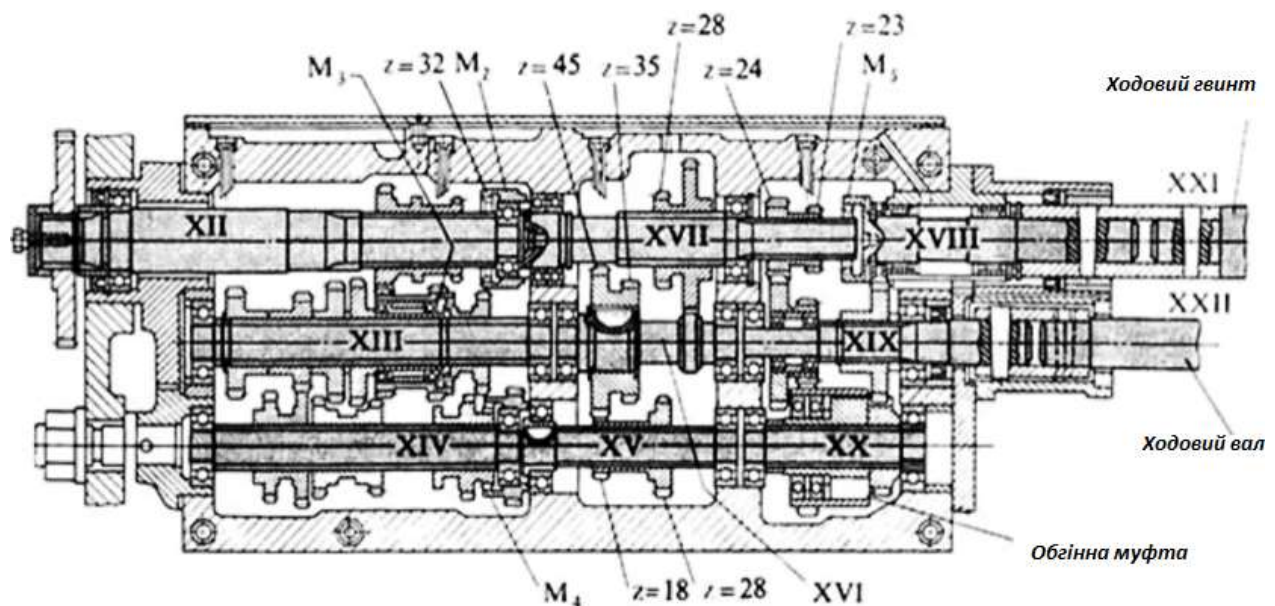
Схема коробки подач токарного верстату 16К20
